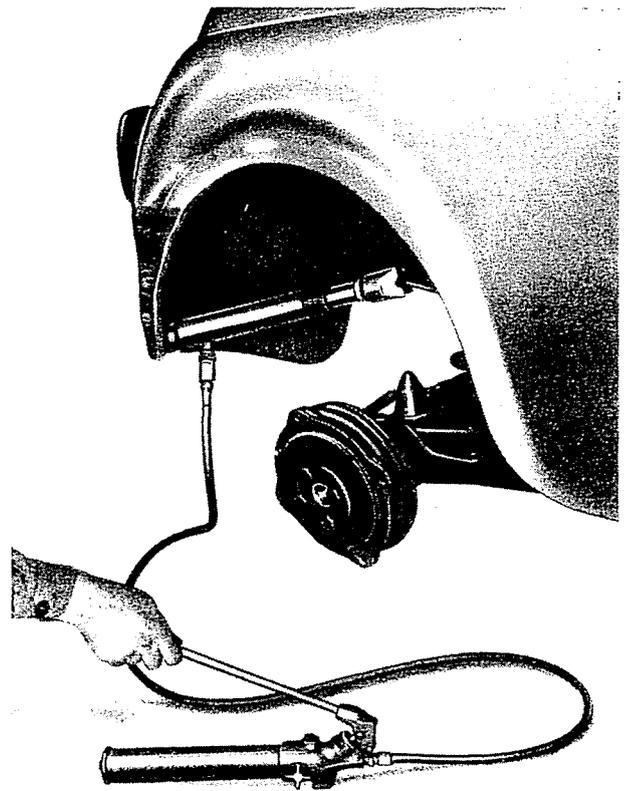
Anbringung des hydraulischen Druckzylinders am Wagen-Hinterteil.
